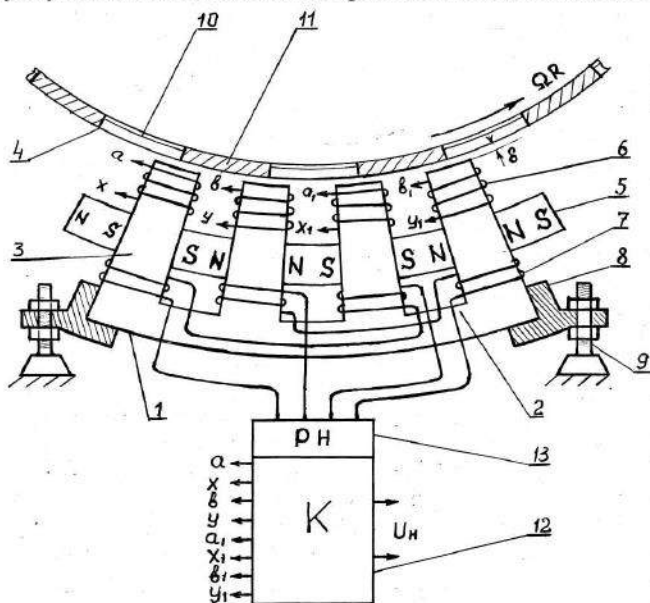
Схема конструкції дугового індукторного електрогенератора: 1 – магнітопровід статора; 2 – спинка магнітопроводу; 3 – полюсний стрижень; 4 – кільцеподібний ротор; 5 – постійні магніти; 6 – якірні обмотки статора; 7 – обмотки збудження; 8 – корпус тримача; 9 – регулювальний гвинт; 10 – обід кільця; 11 – осердя зубця; 12 – комутатор; 13 – регулятор напруги
